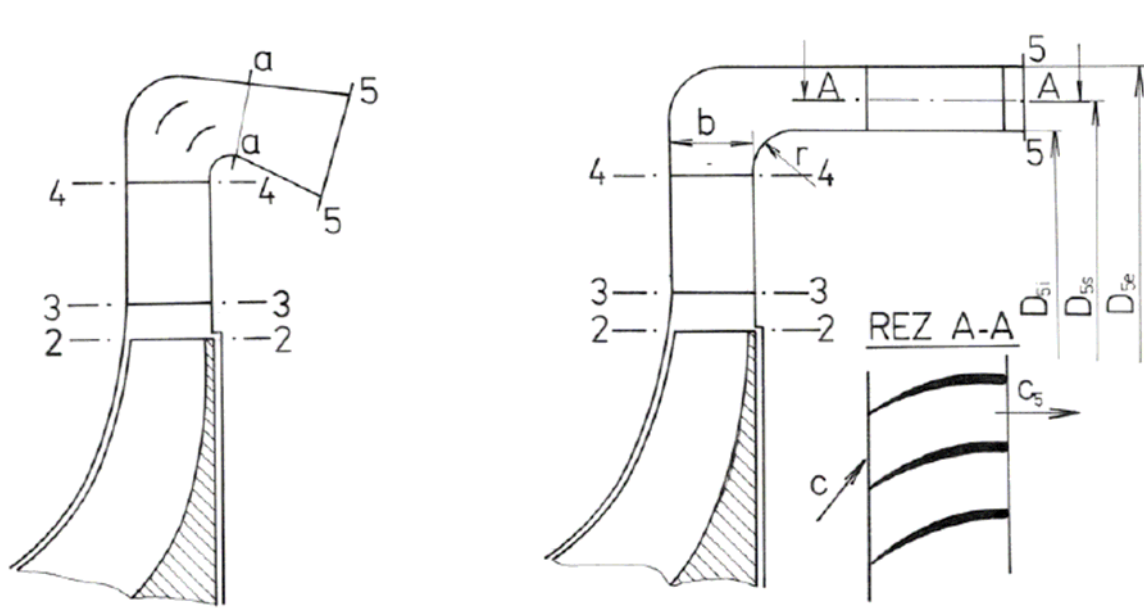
Výstupná sústava radiálneho kompresora motora M-701
